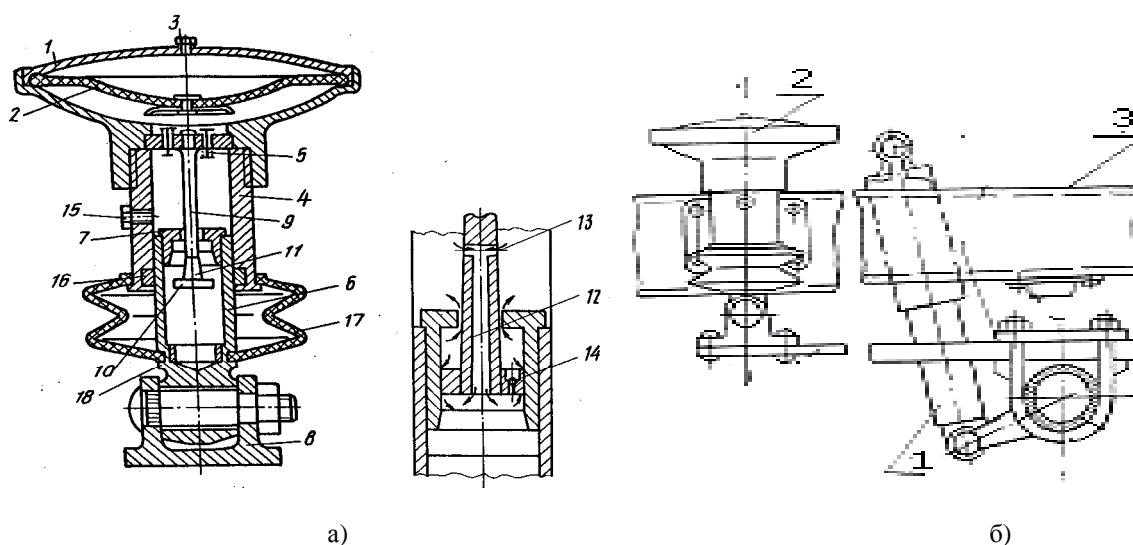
Схема гидропневматического упругого элемента подвески (а) и общий вид подвески (б): а) 1 - газовый баллон; 2 - разделительная диафрагма; 3 - газовый клапан; 4 - цилиндр; 5 - подпружиненный клапан; 6 - пружинный шток; 7 - гильза; 8 - шарнир; 9 - стержень; 10 - цилиндрическая головка; 11 - хвостовик; 12 - осевой канал; 13 - радиальный канал; 14 - обратный клапан; 15 - гидроштуцер; 16 - сегментные магниты; 17 - чехол; 18 - постоянный магнит; б) 1 – амортизатор; 2 - гидропневматический упругий элемент; 3 - рама
